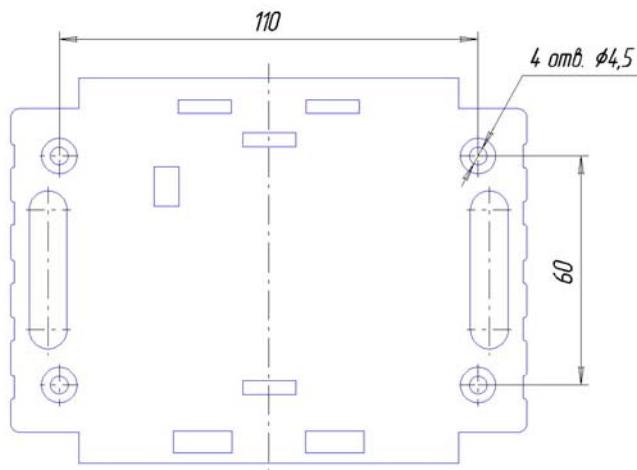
Крепление адресного блока (присоединительные размеры)
